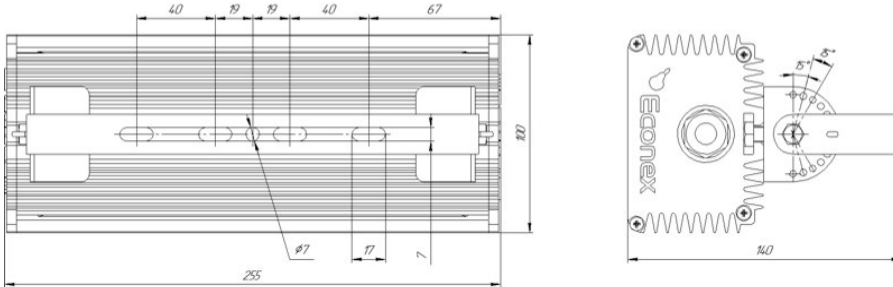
Габаритный и присоединительный чертеж светильника Econex Board 12
